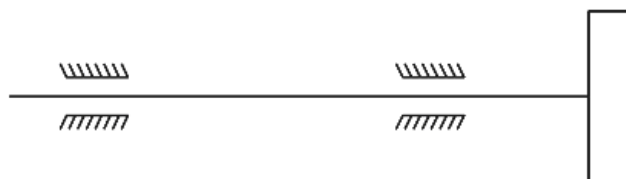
Компоновочна схема шпиндельного вузла верстата
